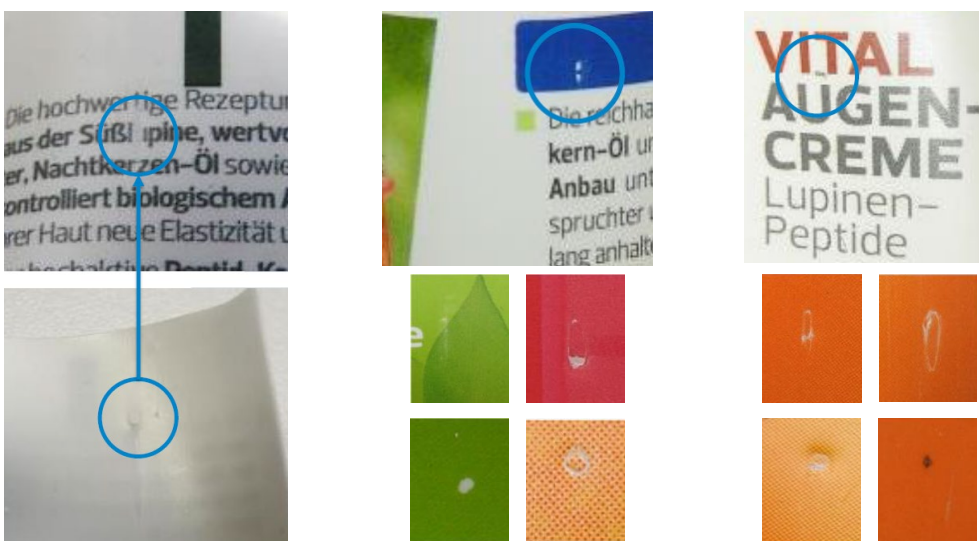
Partikel und Materialeinschlüsse als Störfaktoren für die Dekoration auf der Tubenaußenseite
